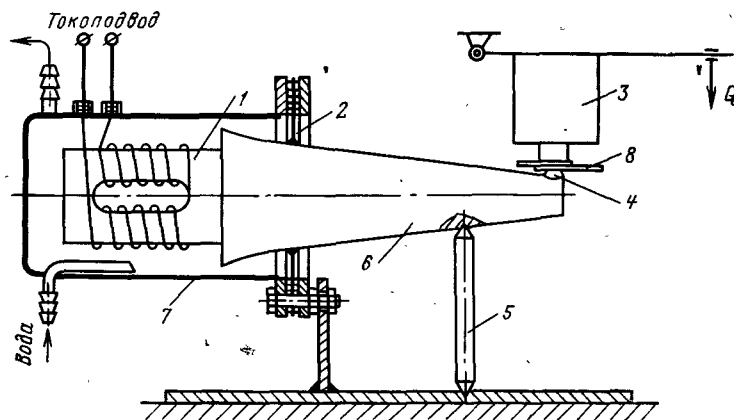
Схема установки для точечной сварки ультразвуком.
